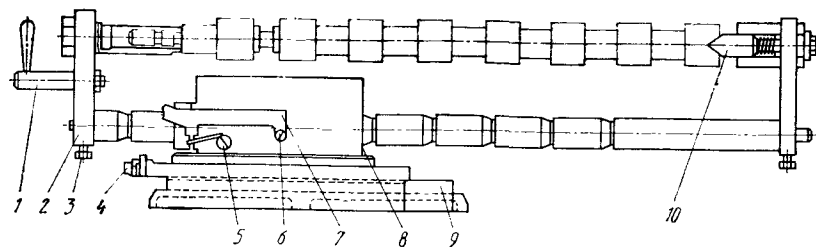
Приспособление для накатки рифлей на рабочих шейках вытяжных цилиндров:
